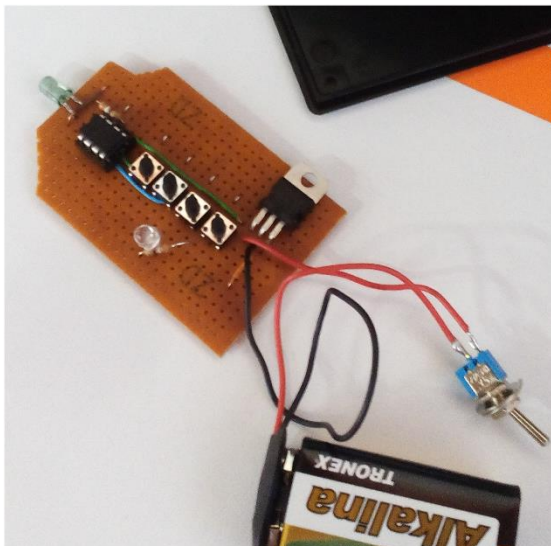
Montaje del circuito transmisor en tarjeta PCB
